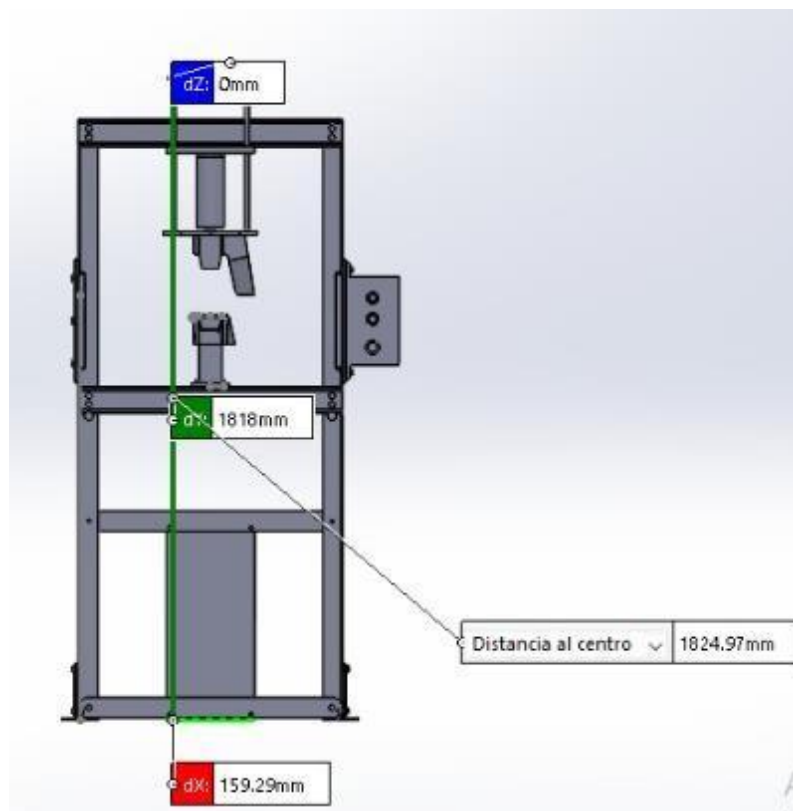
Dimensiones de la dobladora de vista frontal (1818 mm de alto).
